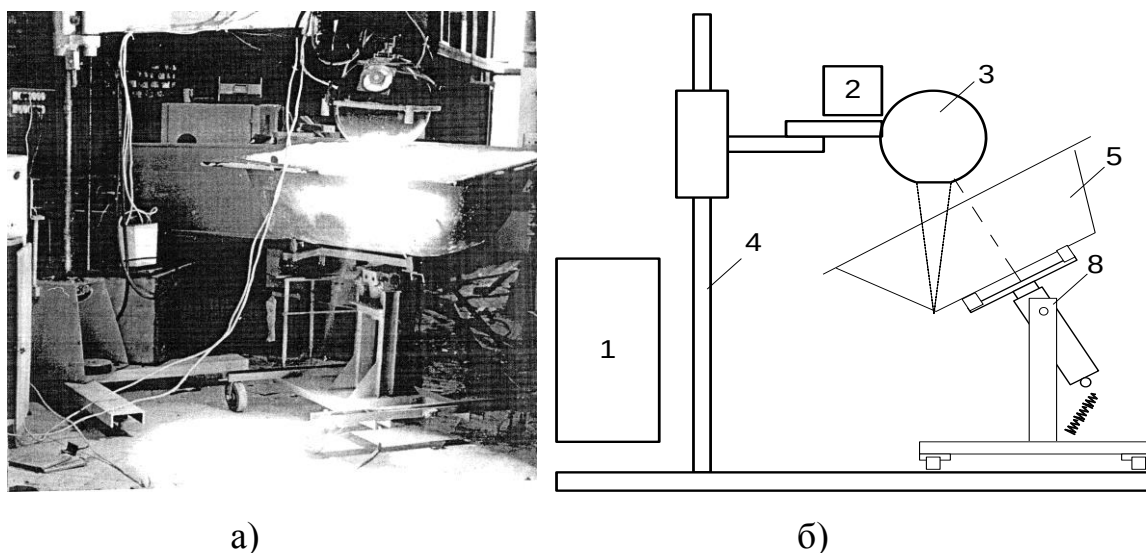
Внешний вид работающей установки (а) и её схематическое устройство (б): источник питания (1), блок поджига (2), генератор лучистой энергии (3), колонна сварочного полуавтомата типа «Т-31021» (4), обрабатываемое изделие (5), поворотная тележка (6)
